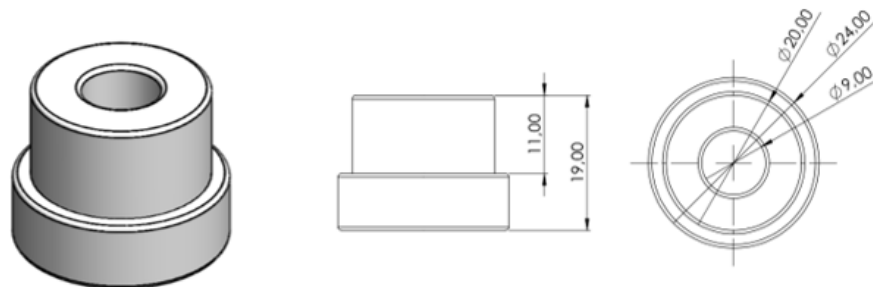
Diseño y dimensiones de los bocines deslizantes. (Fuente Propia)
